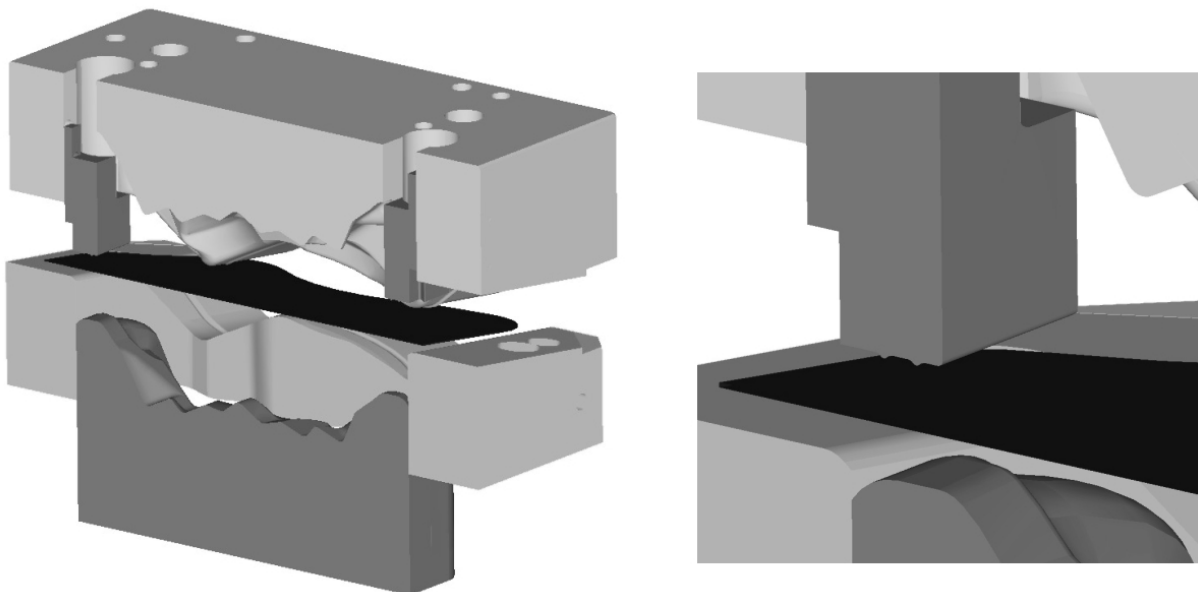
Werkzeugaufbau (links) und Detailansicht des Bremsstempels (rechts)
